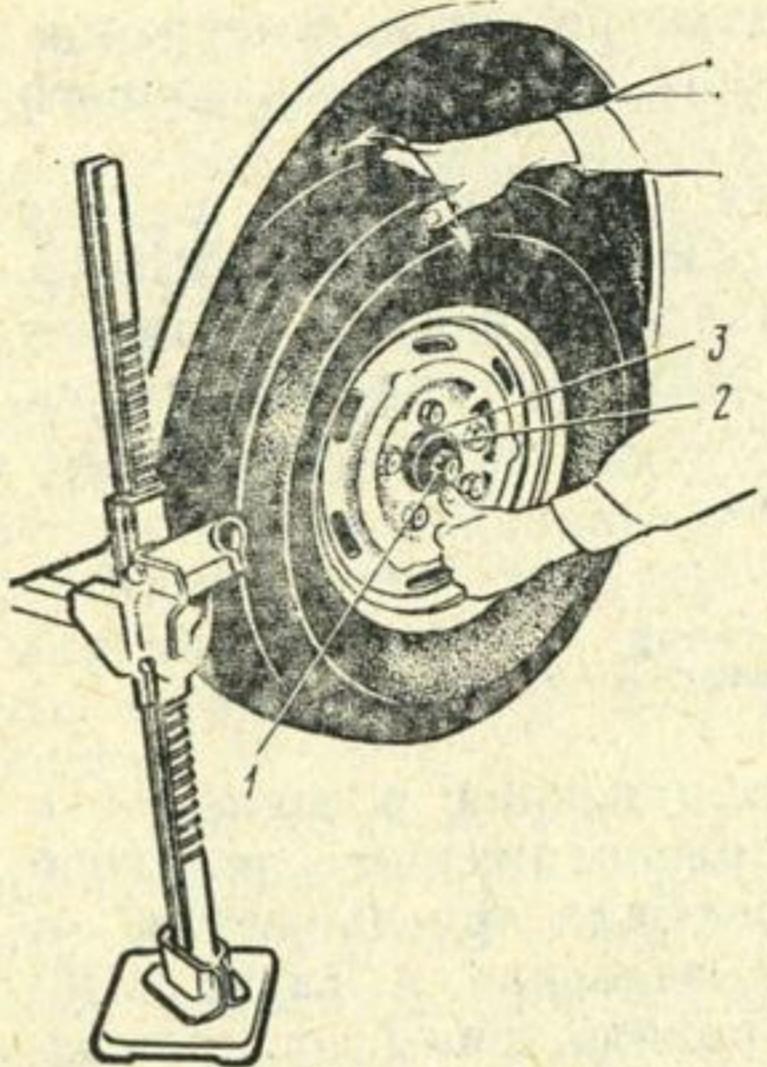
Проверка подтяжки подшипников ступицы переднего колеса:
